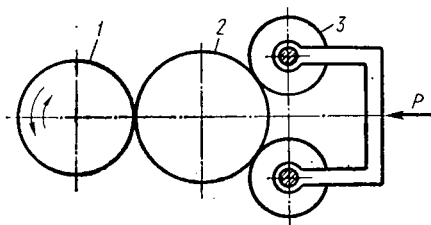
Схема обкатывания цилиндрической шестерни тремя шестернями-эталопами
